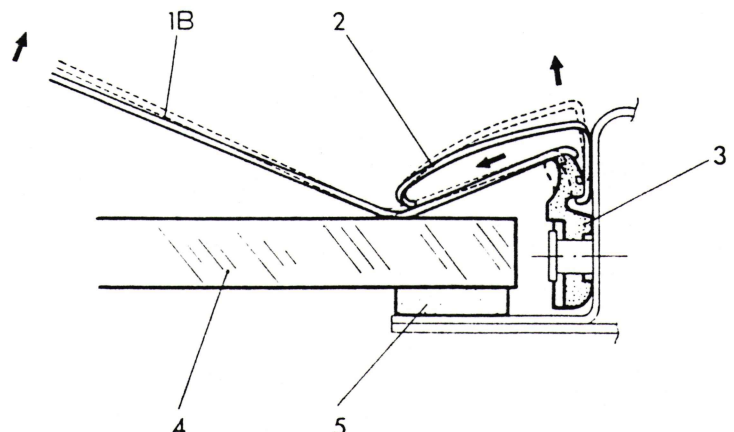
Demonstration der Anwendung der Werkzeuge A. 78032.
